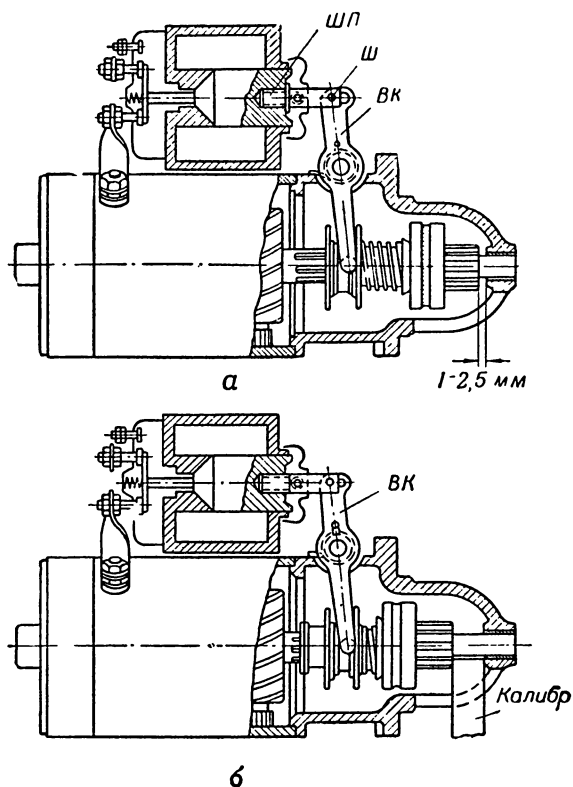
Проверка регулировки привода стартеров типа СЛ и СТ
